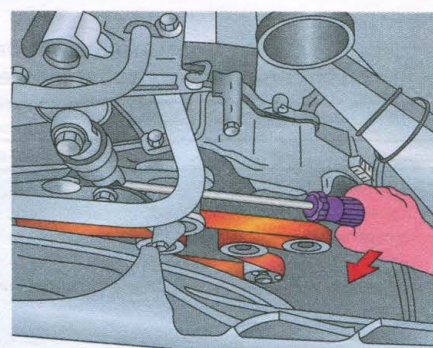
Ослабление натяжения ремня привода агрегатов на двигателе X25DT
